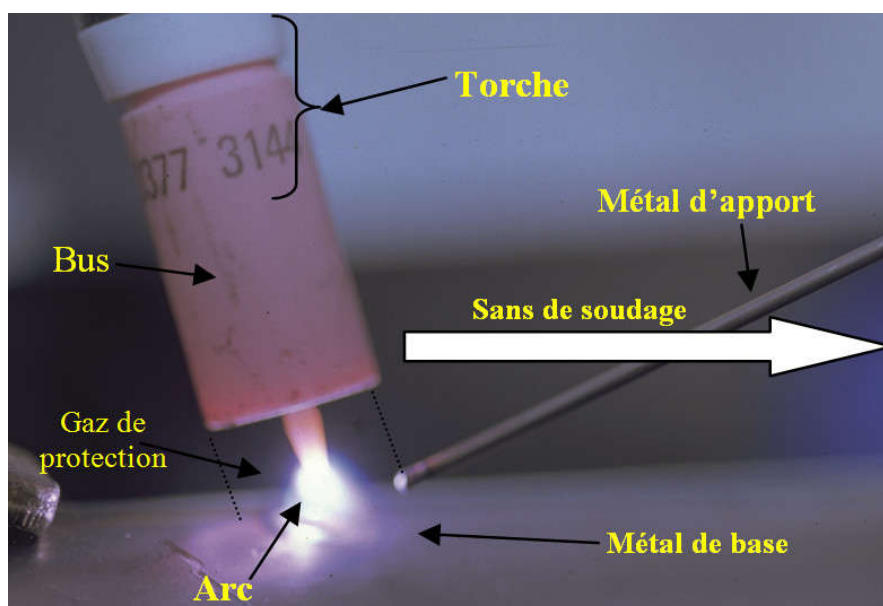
Procédé de soudage à l'arc TIG.
